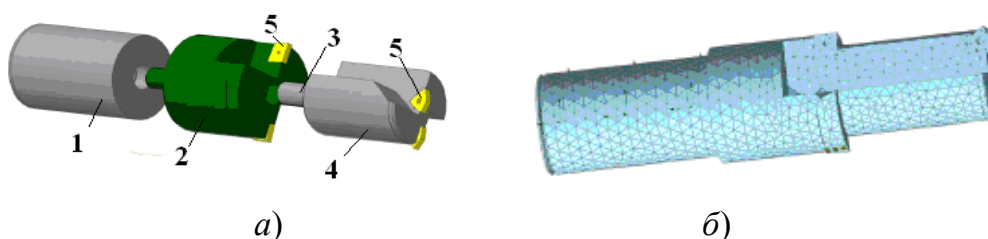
Схемы для расчета НДС двухступенчатого комбинированного инструмента с цилиндрическими соединительной и центрирующей частями:
